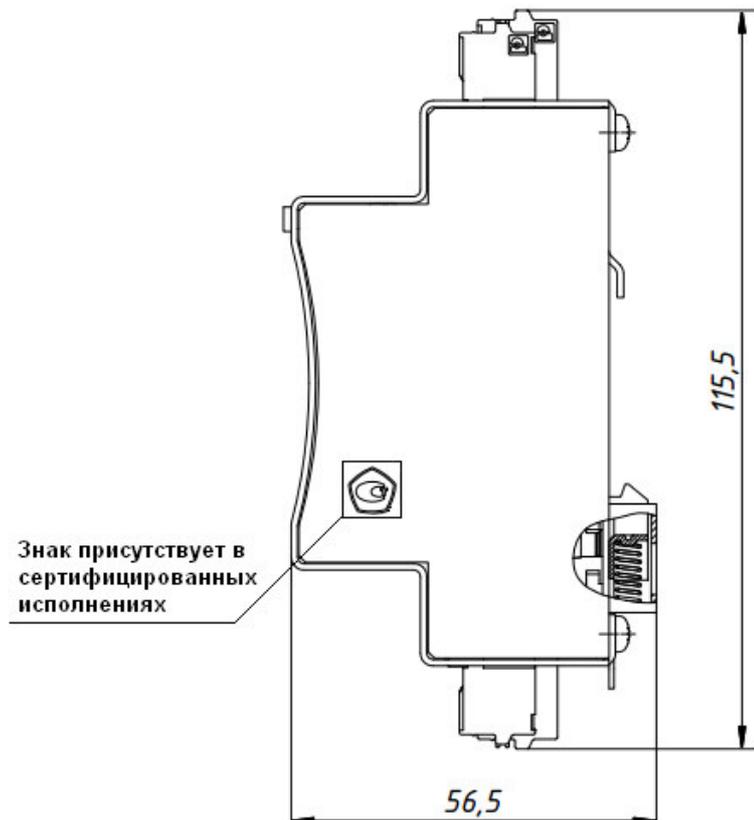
Модуль Элсима-А01. Габаритно-установочный чертеж. Вид сбоку
